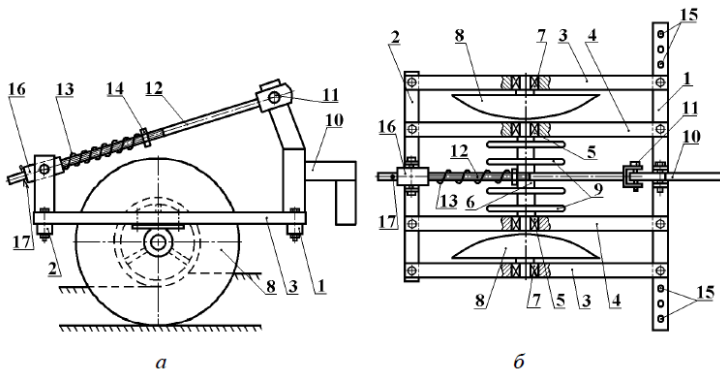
Каток: *а* – вид сбоку; *б* – вид сверху; 1, 2 – балки поперечные; 3, 4 – балки продольные; 5, 7 – подшипники; 6 – ось; 8 – сферические диски; 9 – прикатывающие кольца; 10 – кронштейн; 11 – палец; 12 – штанга; 13 – пружина; 14 – гайка; 15 – регулировочные отверстия; 16 – муфта; 17 – шплинт
